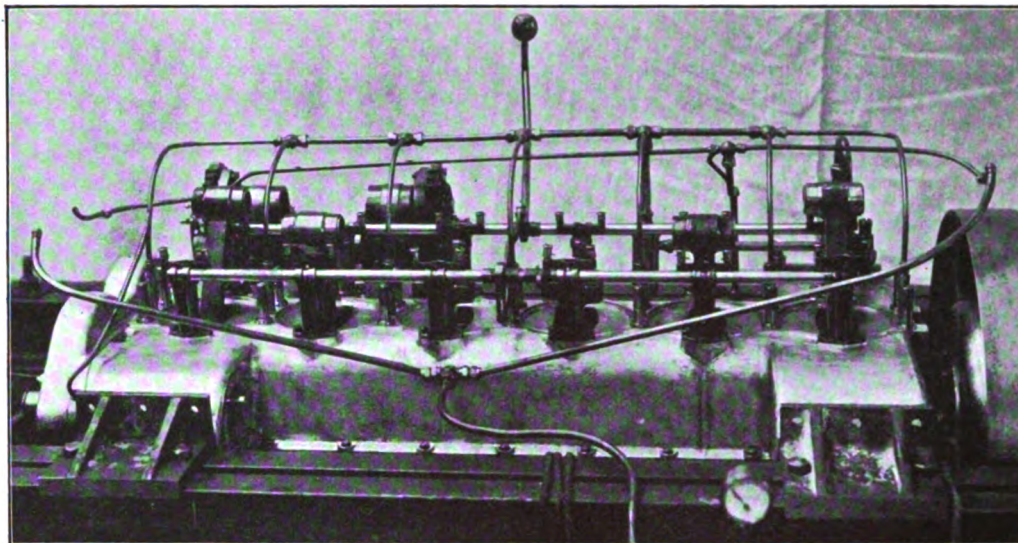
Maybach-Motor ohne Zylinder, Saug- und Auspuffleitung.
